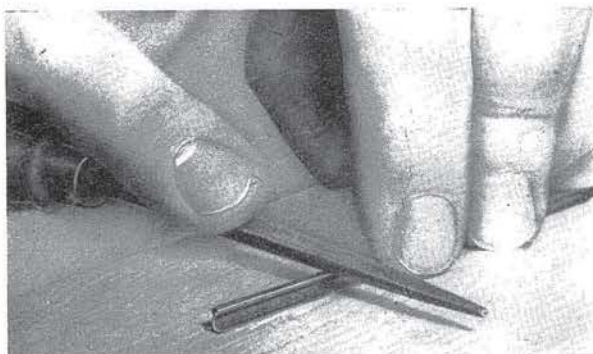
Die hohle Profilschiene wird mit einer Dreikantfeile eingefeilt.
